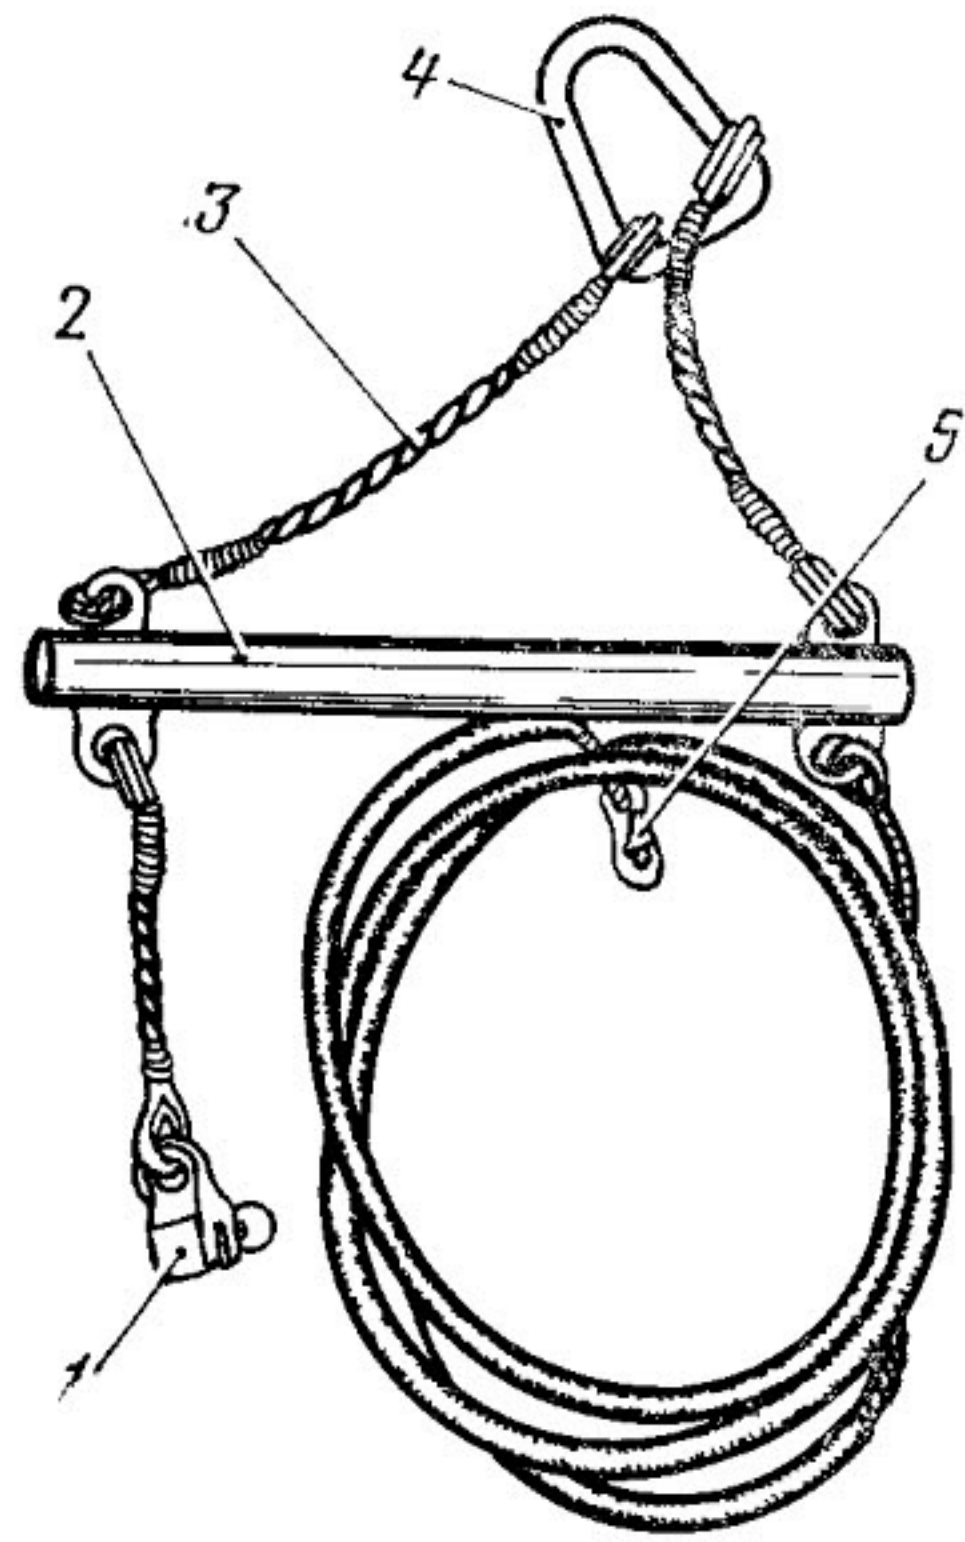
Приспособление для подъема и снятия свободной турбины двигателя:
